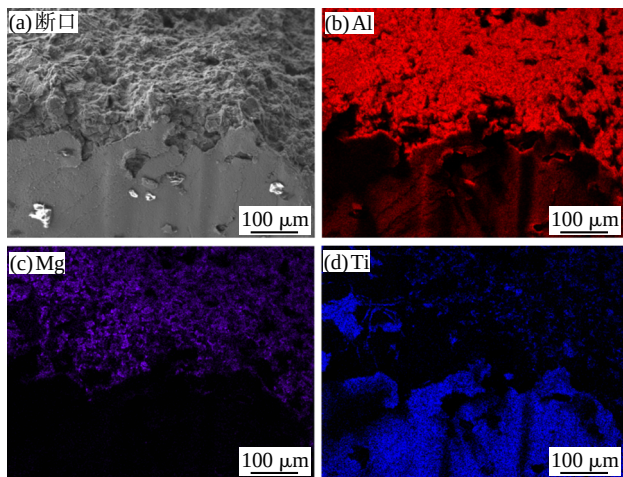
MIG 焊试样拉伸断口的形貌和元素面扫描图
